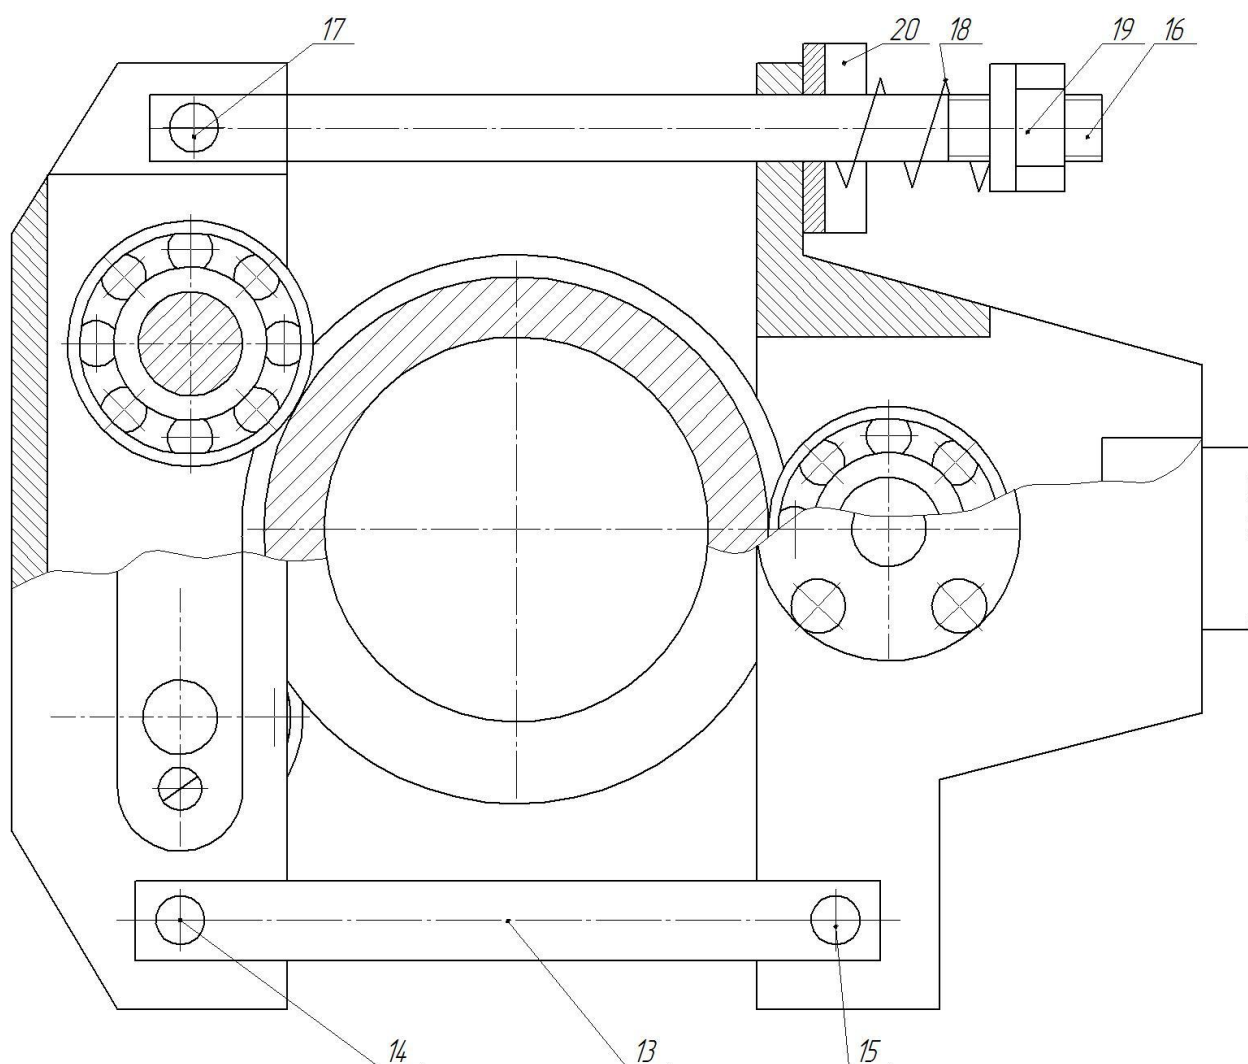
Вид сбоку правящего ролика по а.с.№1682149
